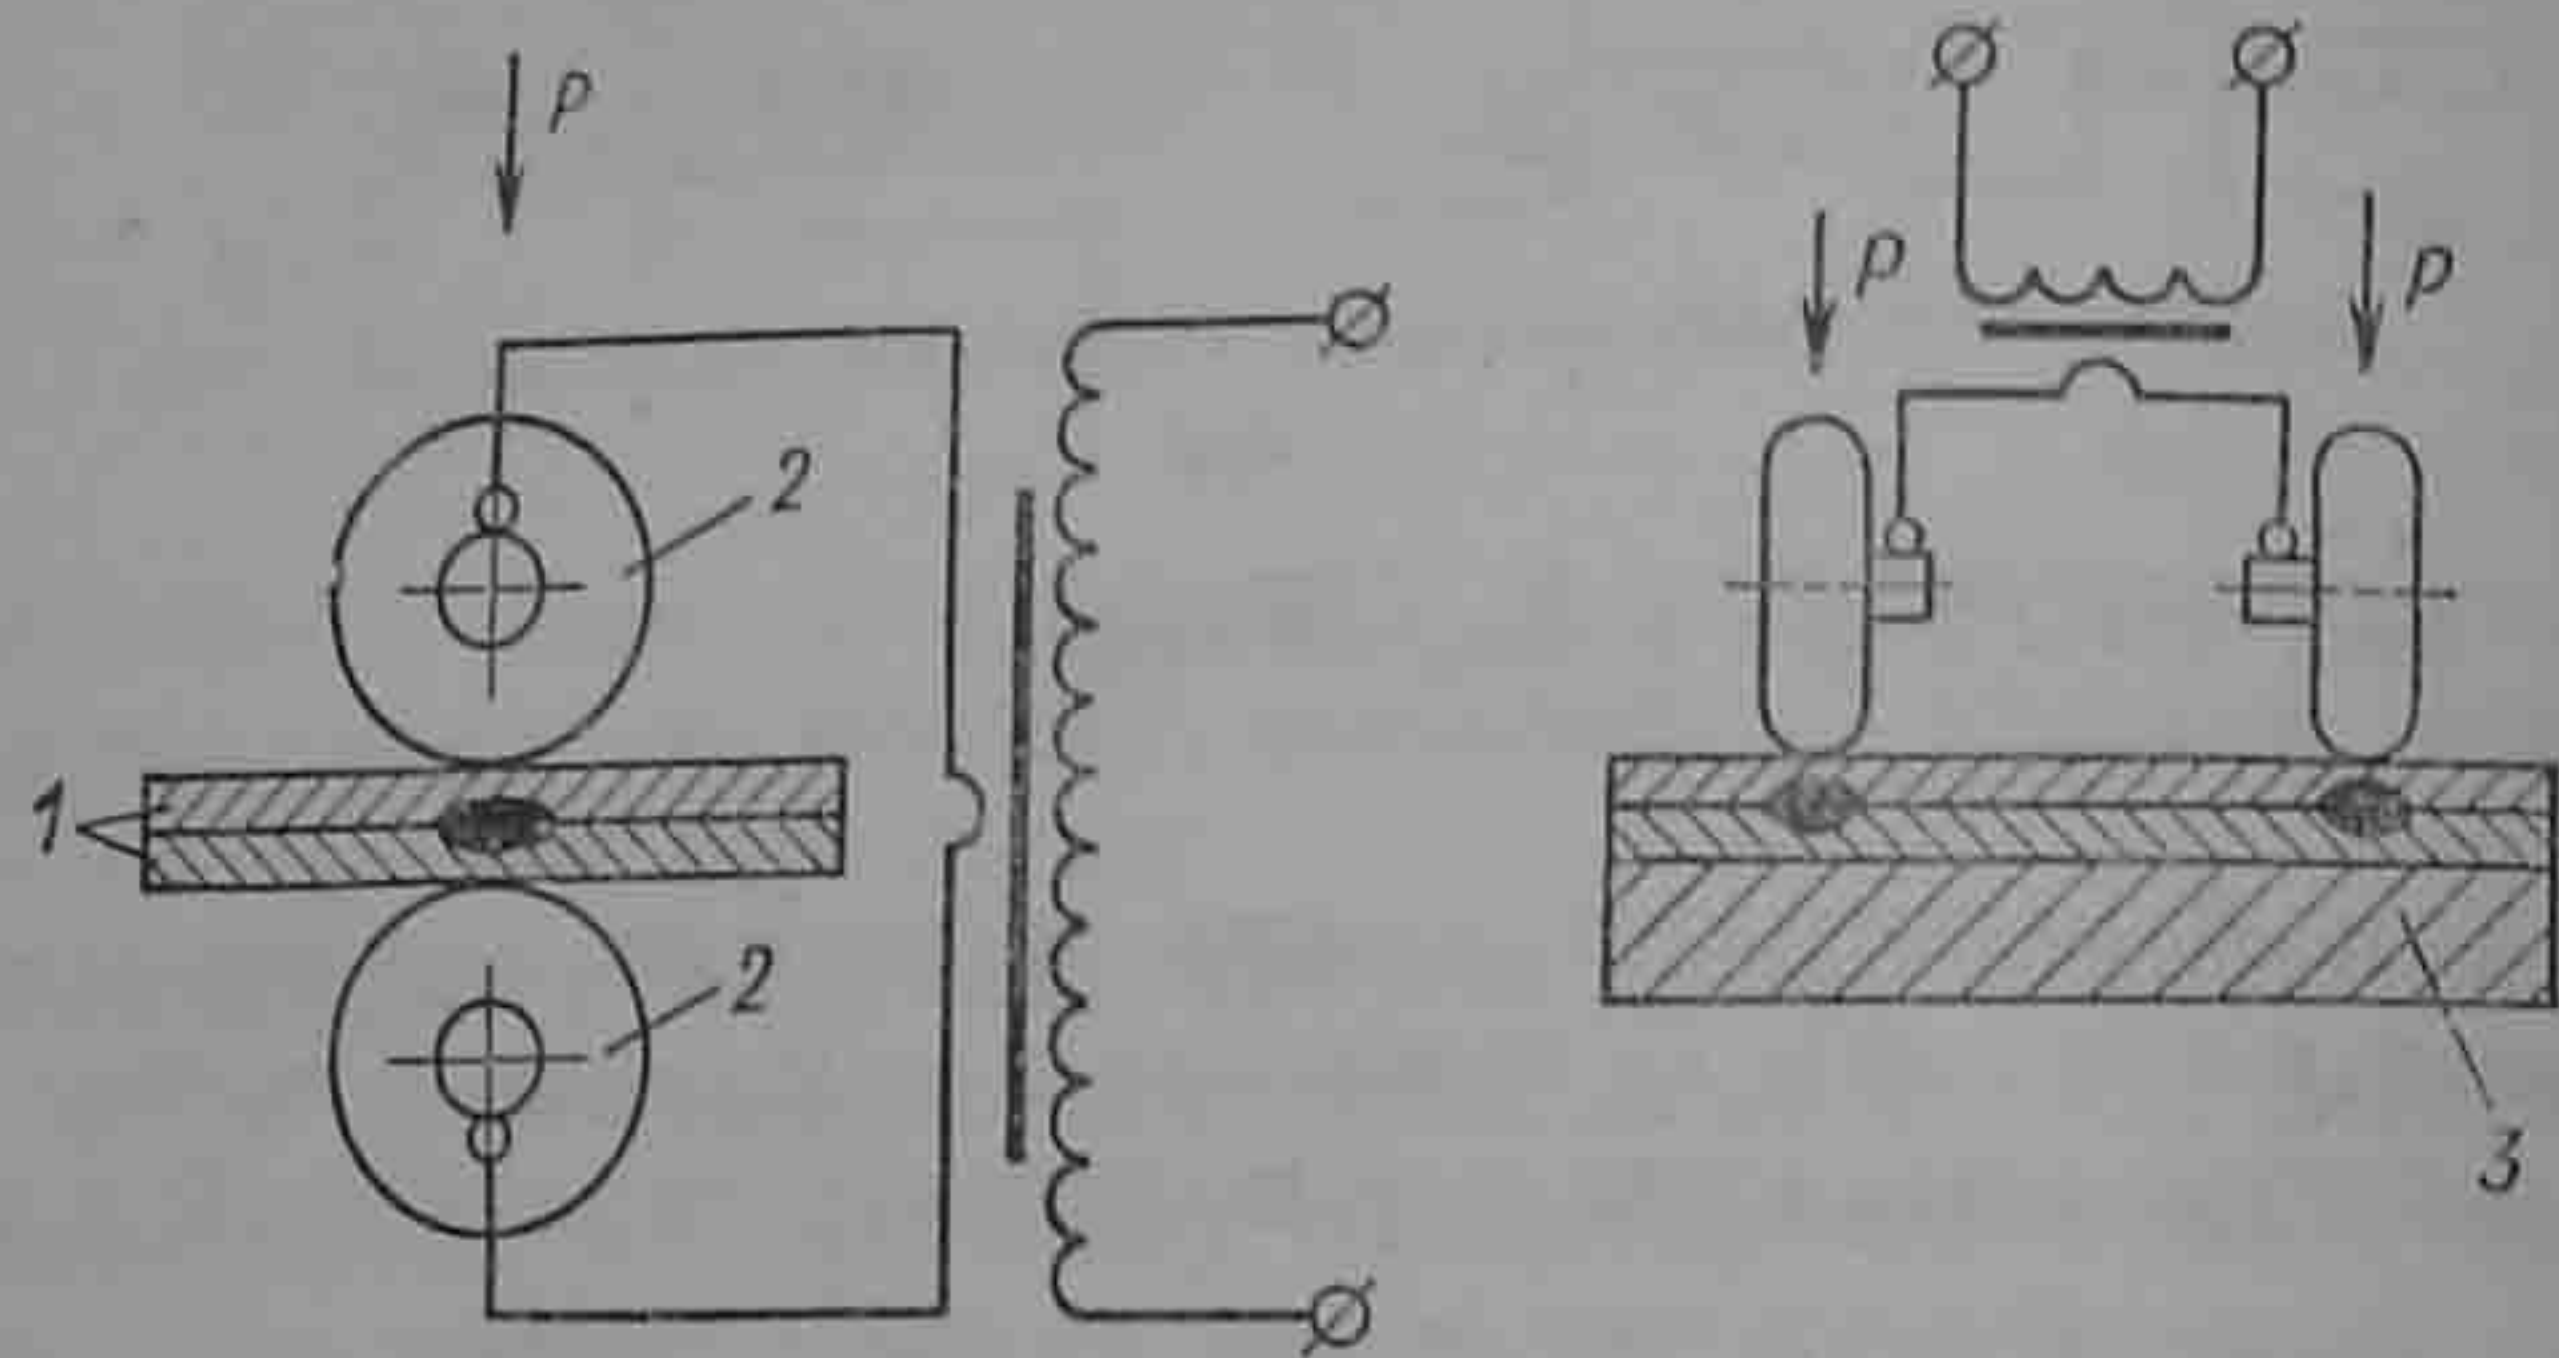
Принципиальная схема шовной сварки:
